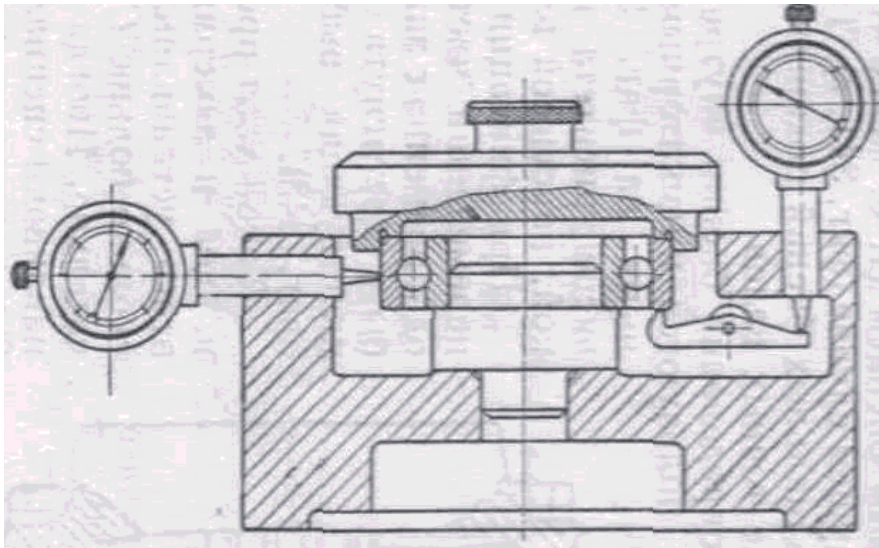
Приспособление для контроля радиального и осевого биения подшипника
